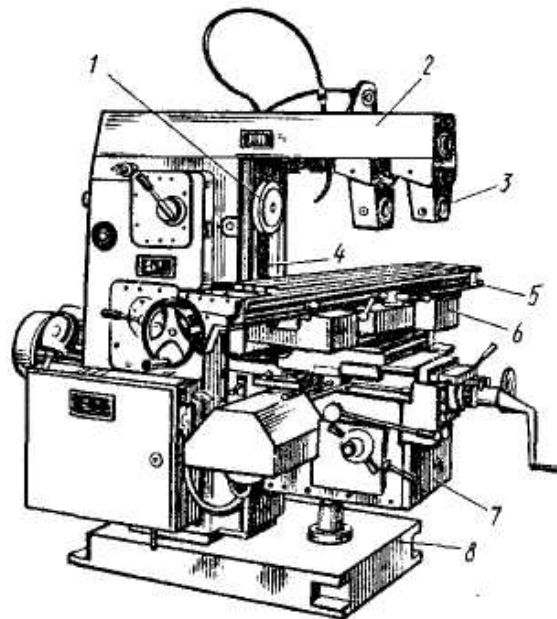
Горизонтально-фрезерный станок: 1 – шпиндель; 2 – хобот; 3 – подвеска; 4 – станина; 5 – стол; 6 – каретка; 7 – консоль; 8 – фундаментная плита
